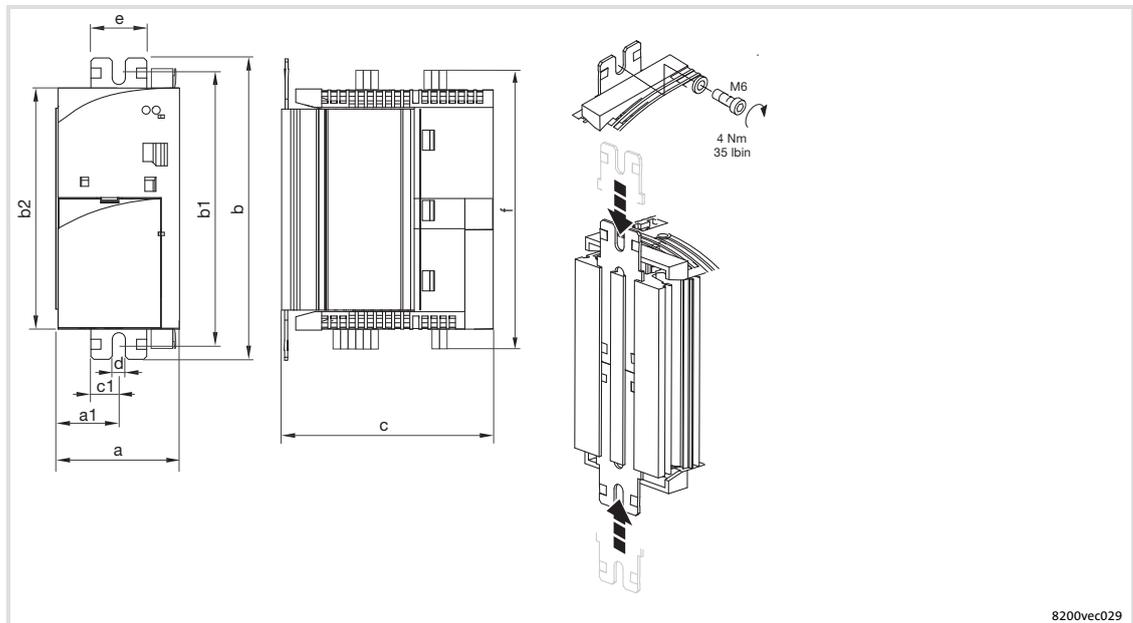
Abmessungen Montage in "Cold Plate"-Technik 0.25 ... 2.2 kW
